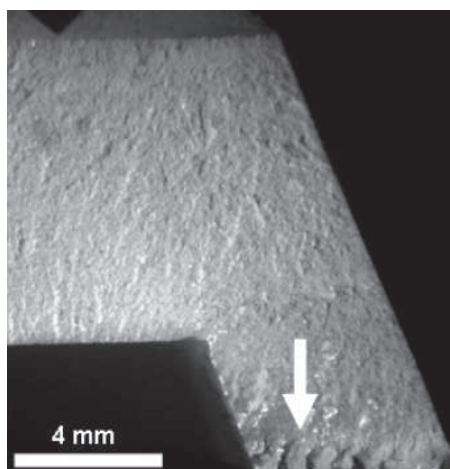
Superficie de fractura, zona C. La flecha indica la zona de fractura intergranular
